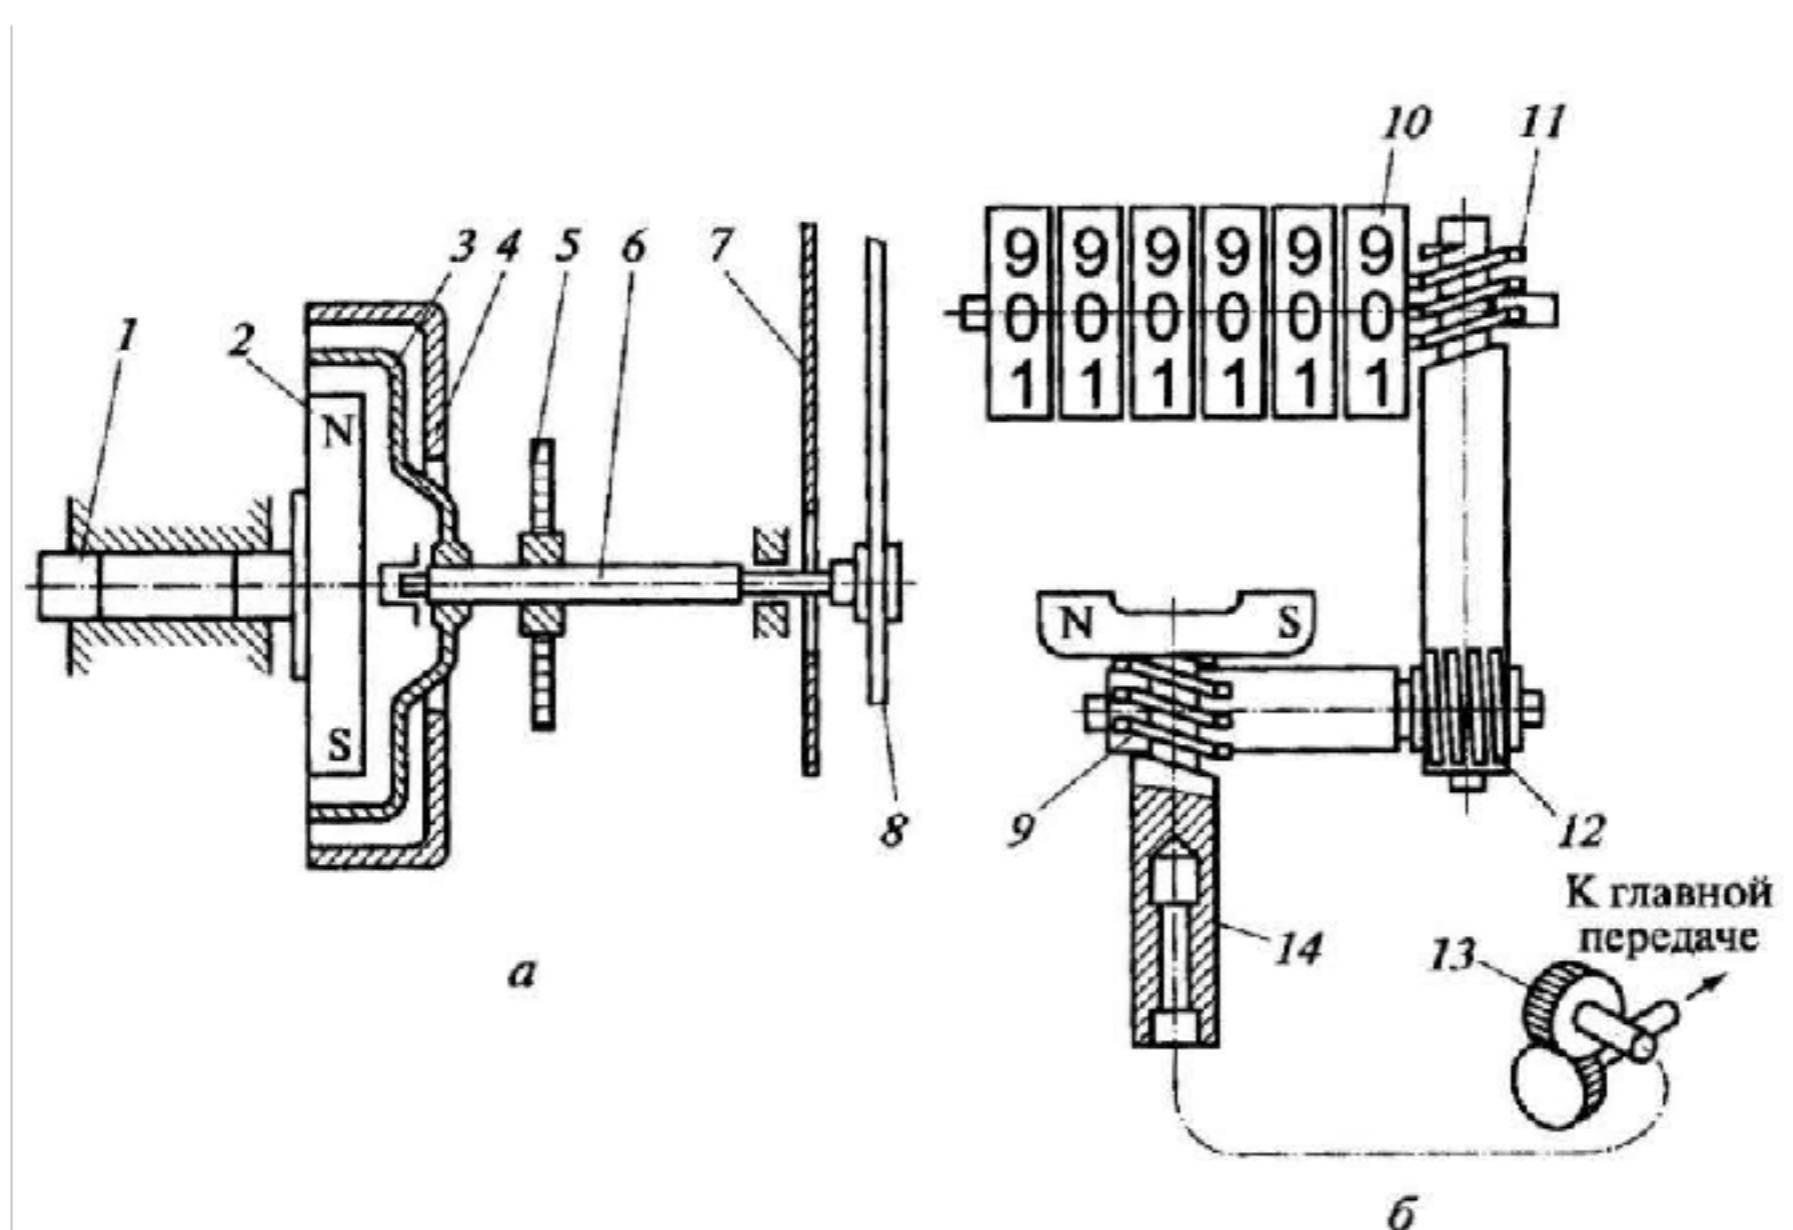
Схема действия спидометра с приводом от гибкого вала: а — магнитоиндукционный скоростной узел; б — привод счетного узла; 1 — приводной валик; 2 — постоянный магнит; 3 — алюминиевая картушка; 4 — магнитный экран; 5 — возвратная пружина; 6 — ось стрелки; 7 — шкала; 8 — стрелка; 9 — ведущий червяк; 10 — начальный барабанчик счетного узла; 11 — ведомый червяк; 12 — промежуточный червяк; 13 — винтовой редуктор; 14 — входной валик
